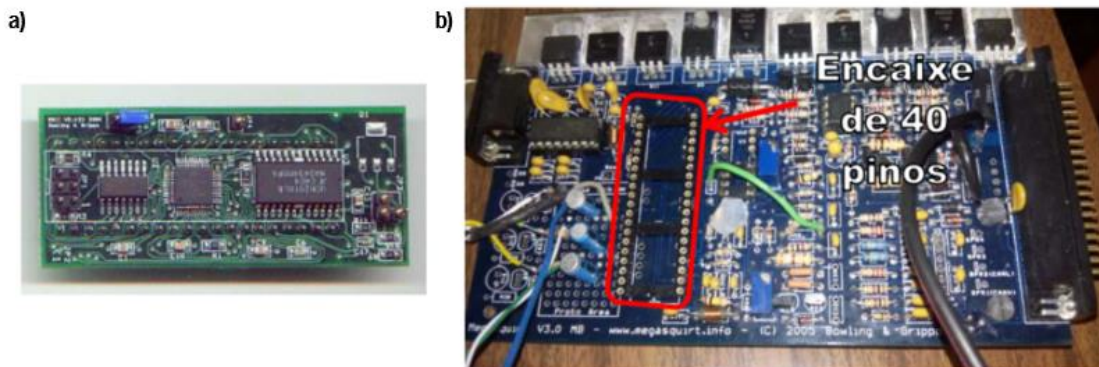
a) PCB com processador MC9S12C64; b) placa mãe V3.0 (adaptado de [17])
